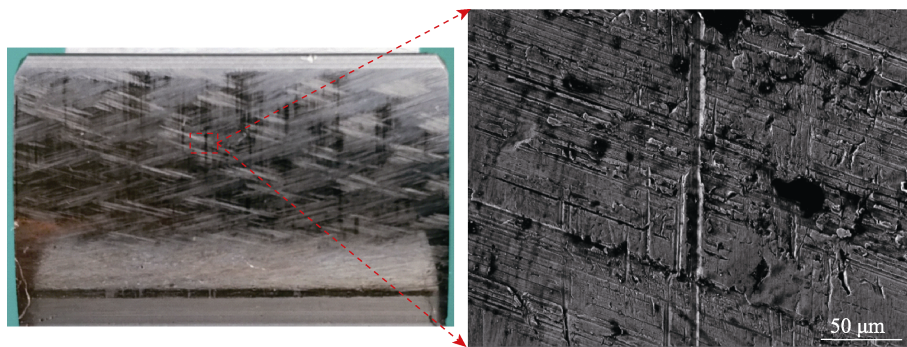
传动油润滑下试验齿轮 8 级测试后磨损形貌
